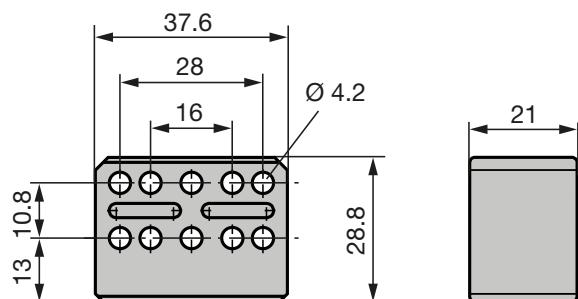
Dimensions de montage du capteur de position BTL6-A-3800-2
